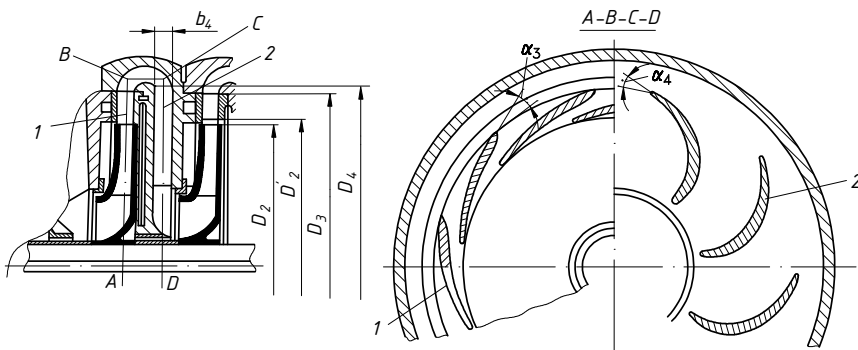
Двухступенчатый центробежный насос: 1 – кольцевой лопаточный направляющий аппарат; 2 – обратный направляющий аппарат
